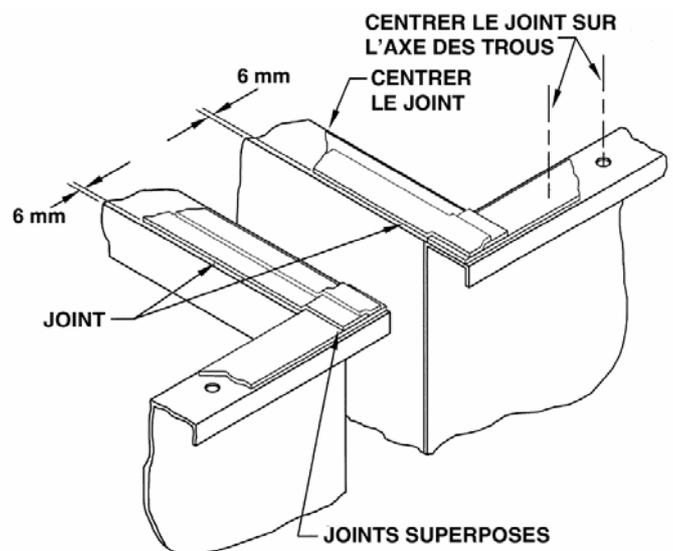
Détail du joint pour les Unités avec Deux sections ou Plus.
